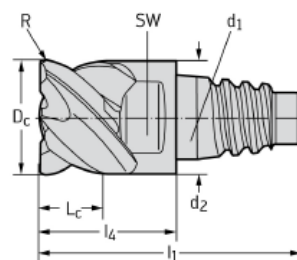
Cap de frezat din carbură metalică MC326.25.4E5P318-WJ30TF [4]
